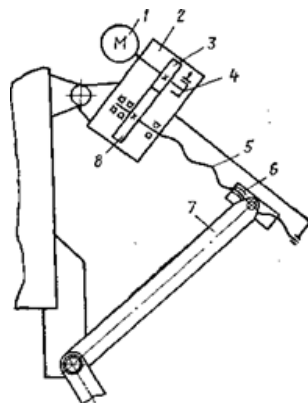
Кінематична схема механізму приводу плеча робота
